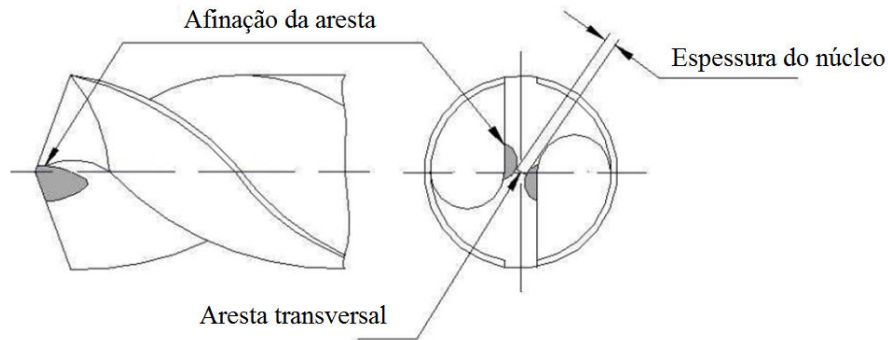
Afinação da aresta transversal de corte (OLIVEIRA, 2008)
